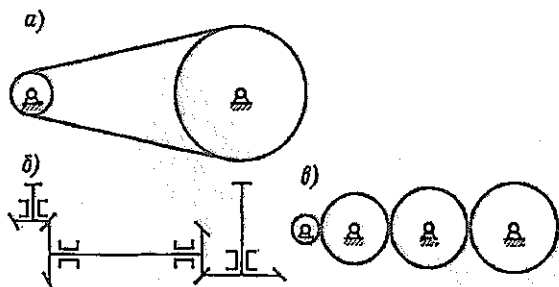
Кинематические схемы передач: а — гибкой связью; б — с коническими зубчатыми колесами; в — с цилиндрическими зубчатыми колесами
